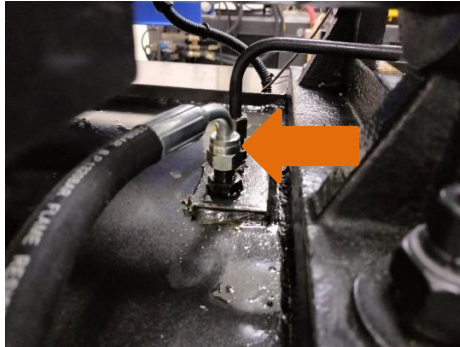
Silinder Sudah Terpasang Kembali Pada Mesin Molding
